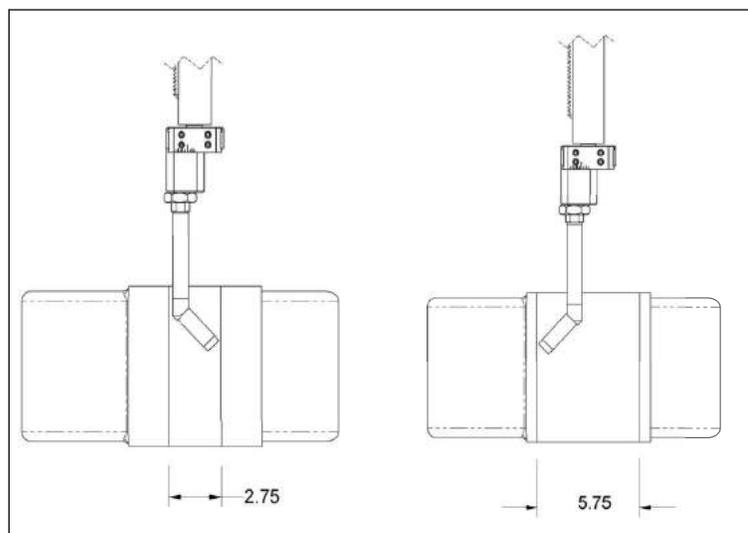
ГОРЕЛКА, УСТАНОВЛЕННАЯ В ПОВОРОТНОЙ ГАЙКЕ
